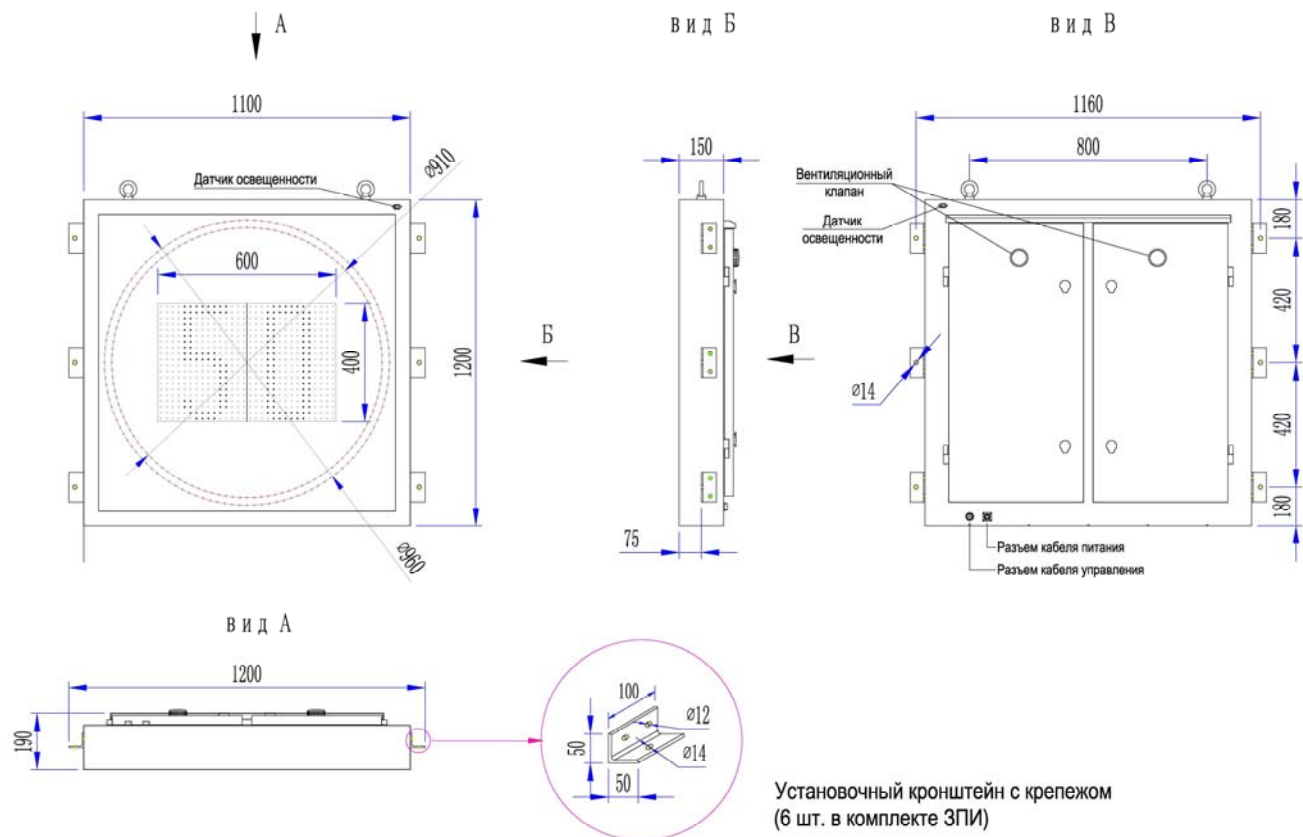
Внешний вид и основные размеры ЗПИ ZOS R20W-110120
